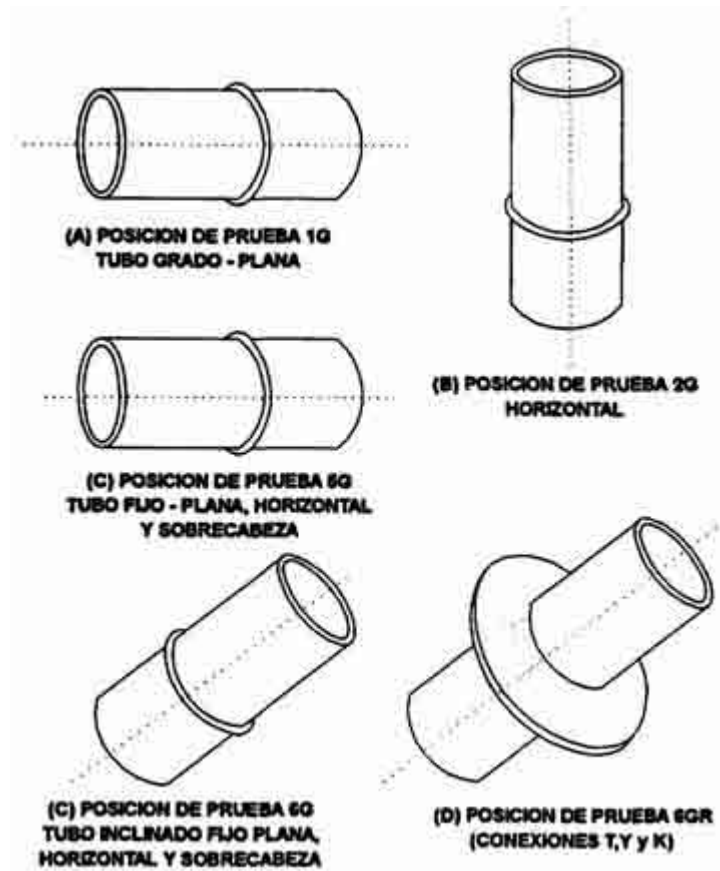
Soldaduras a Tope en Tubería
